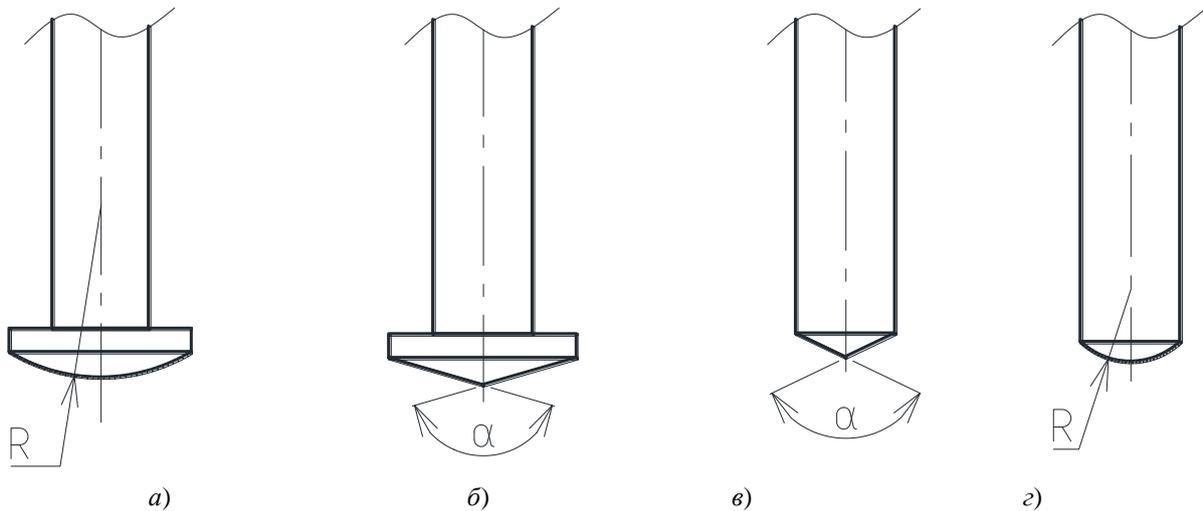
Различные формы подготовки торцов стержней под сварку
